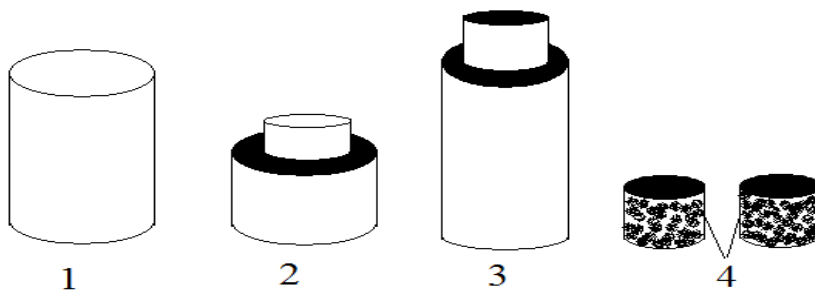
Формовочные детали установки для брикетирования металлотермического топлива. 1 – металлическая цилиндрическая форма – труба; 2 – металлическая форма основания цилиндрической формы – трубы; 3 – металлическая форма для трамбовки шихты брикета; 4 – полученные брикеты
